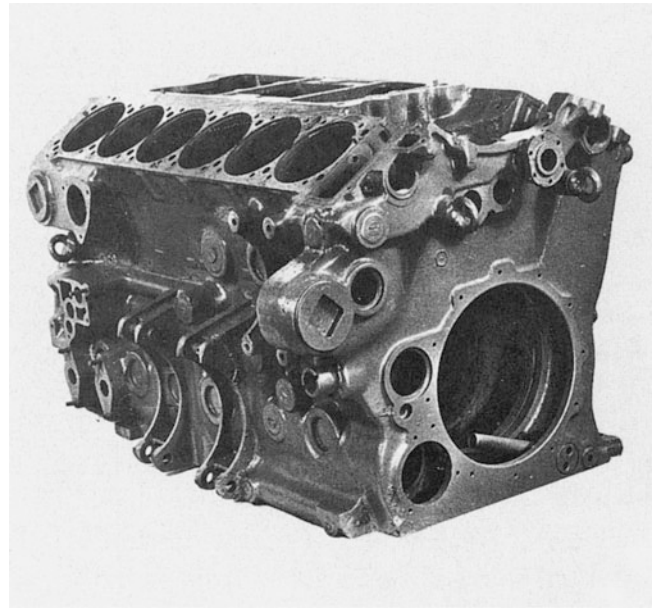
Tunnelgehäuse des Motors HL 230. Die Gehäuse des HL 230, der GTO- und anfangs auch der MD-Motoren wurden gegossen. Später wurden die Gehäuse der MD-Motoren aus Stahlgussteilen und Stahlblechen geschweißt, ebenso die der MC-Motoren
